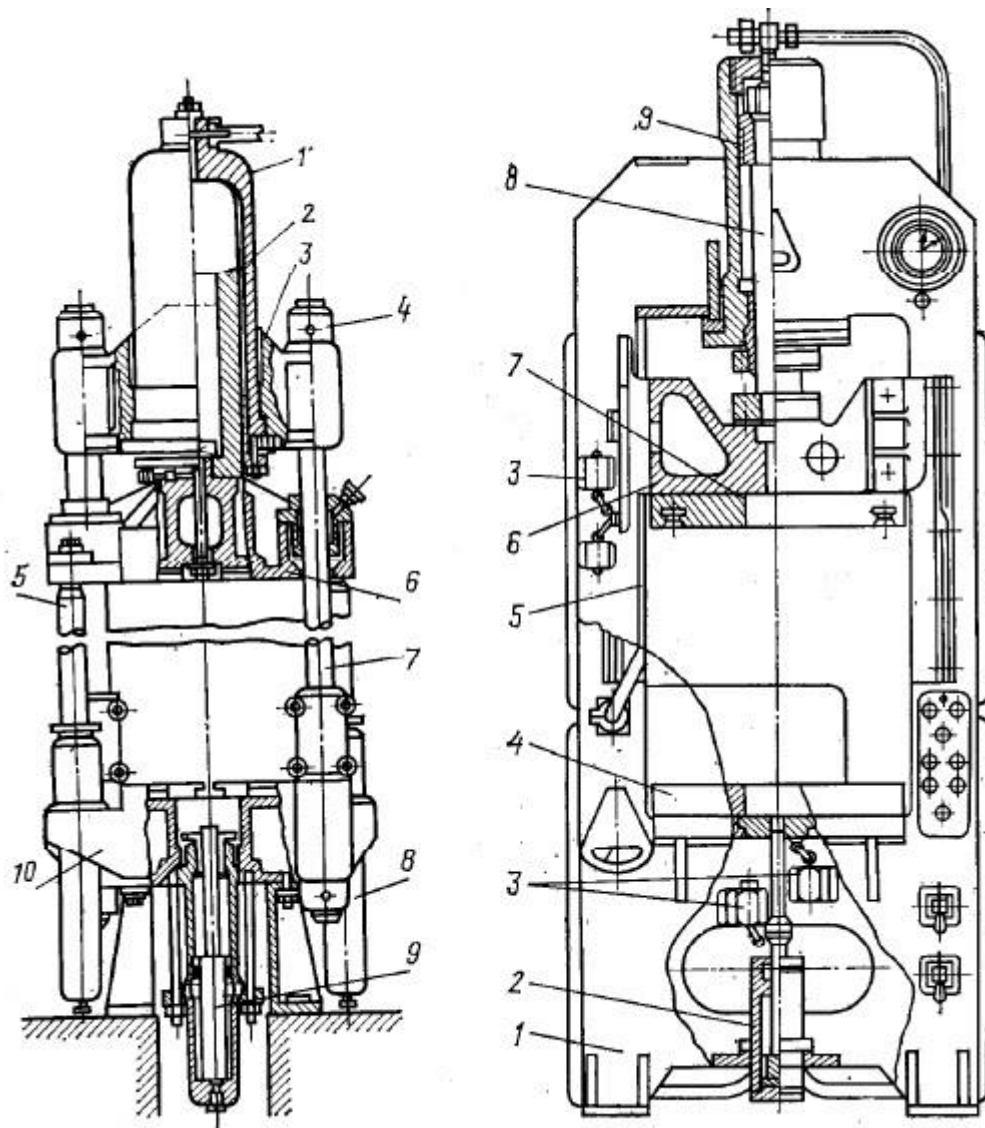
Приклад конструкції гідравлічного колонного преса з верхнім розташуванням робочого циліндра:
